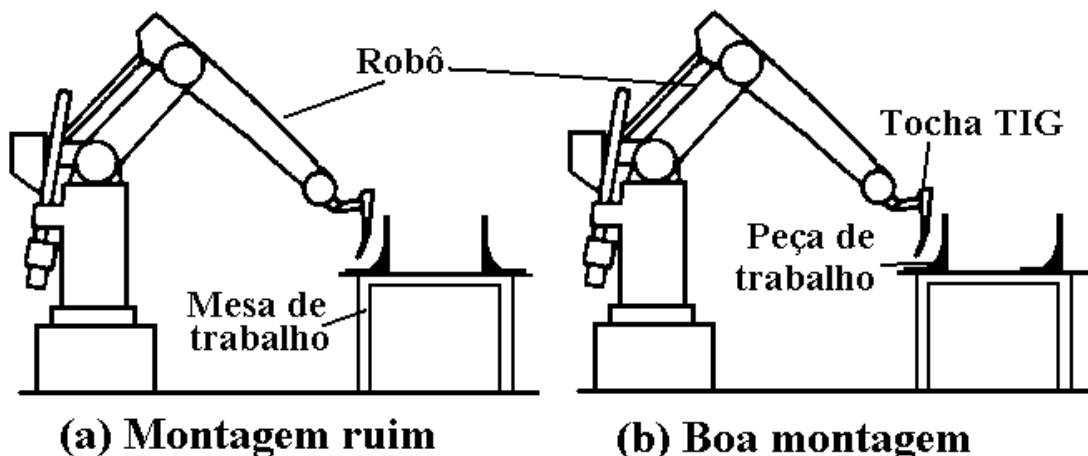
Exemplos de recomendável e não recomendável para soldagem robotizada.
